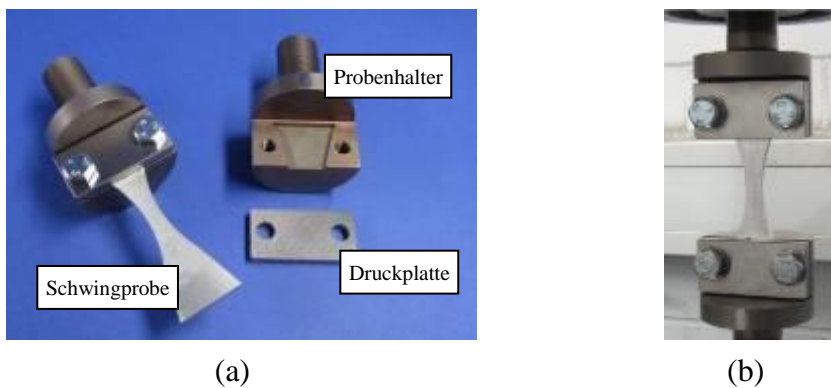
Probenhalter für die Schwingproben (a) und Einbauzustand der Schwingprobe (b)
